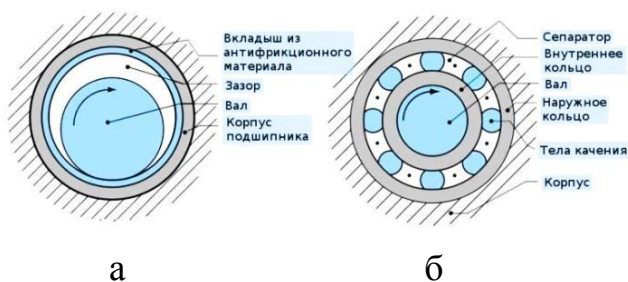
Подшипник скольжений (а) и подшипники качения (б)
